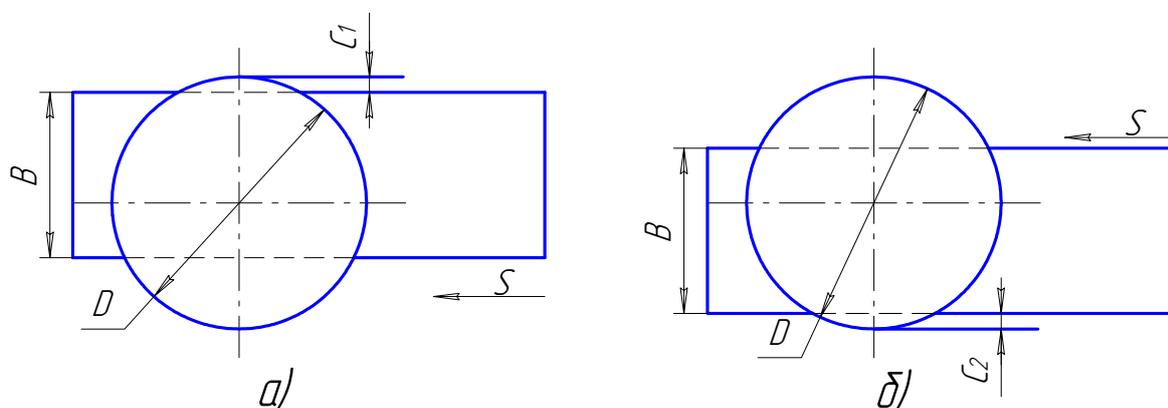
Расположение стальной заготовки при торцевом фрезеровании относительно фрезы: а – врезание зуба фрезы при  $C_1=(0,03...0,05)D$ ; б – выход зуба фрезы при  $C_2=0$ .
